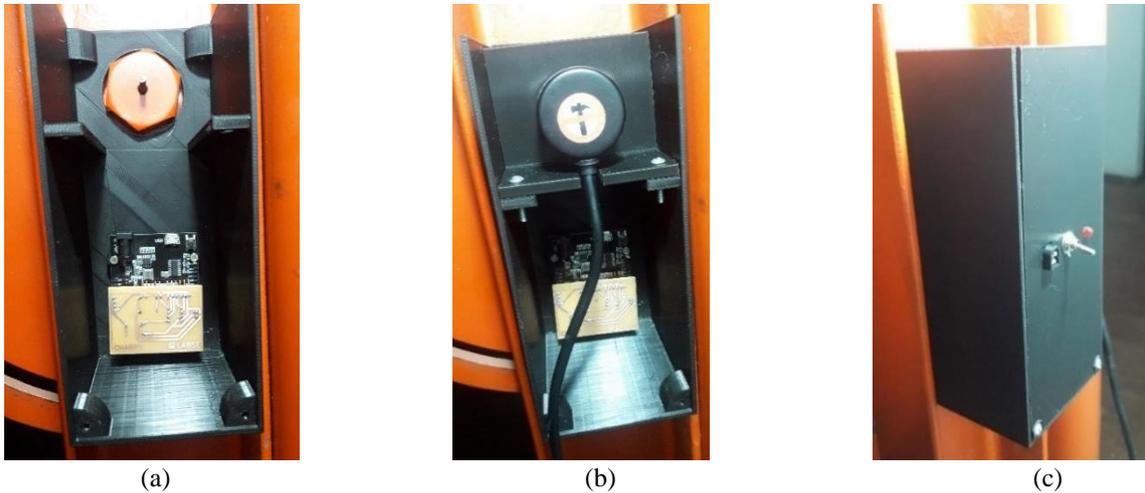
Montaje del sistema de adquisición local a la maquina Charpy.
